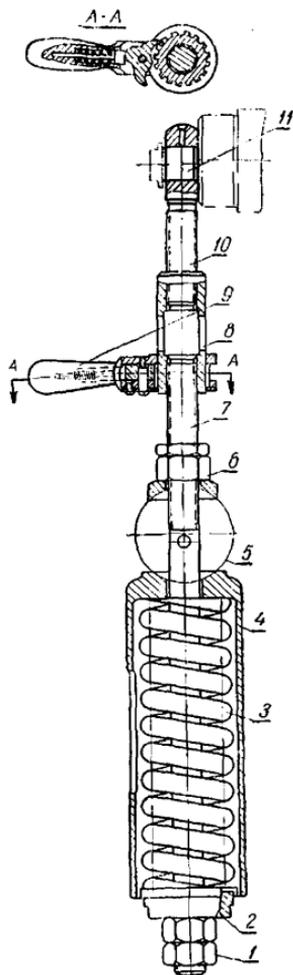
Механизм настройки параллельности валцов станка ЗМ.
